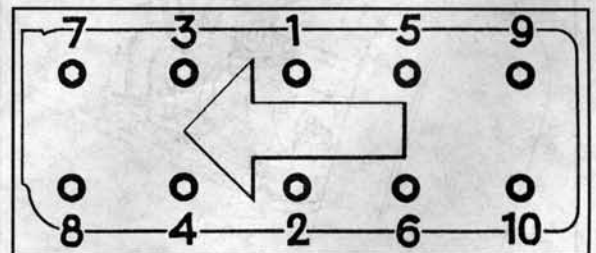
Очередность затяжки болтов головки блока цилиндров двигателя В19
